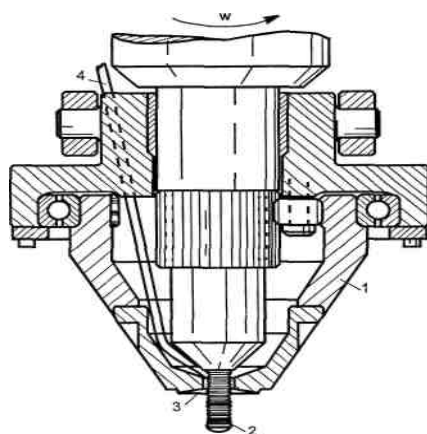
Инструмент для СТП с регулируемым вылетом рабочего стержня относительно опорного бурта, вращением их в разных направлениях (от одного привода) и подачей в зону сварки присадки
